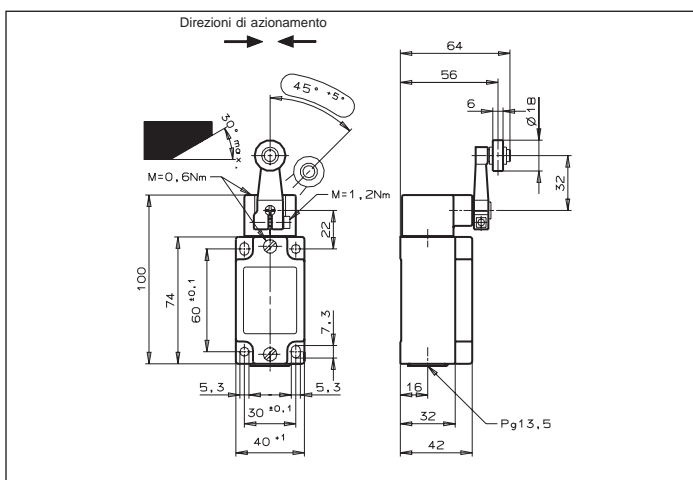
Disegno quotato i100-R1 versione a morsetti
